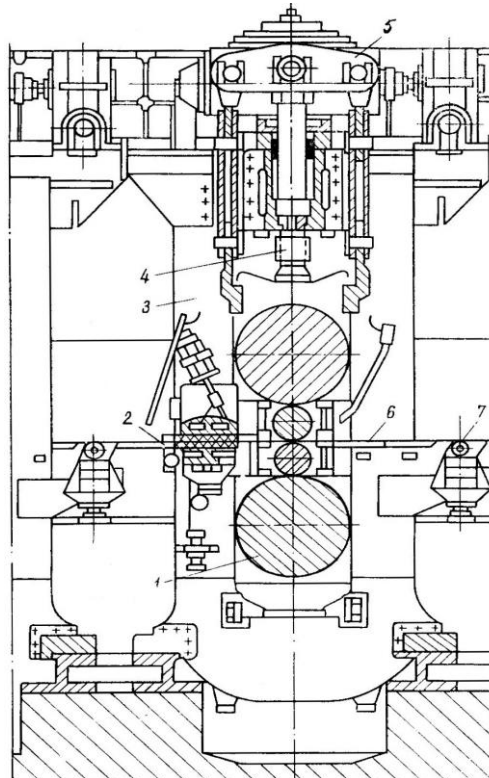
Робоча кліть: 1 – опорні й робочі валки з подушками; 2 – проводковий стіл; 3 – станина робочої кліті; 4 – натискний гвинт; 5 – пристрій, що врівноважує; 6 – проводка; 7 – натяжний ролик.
